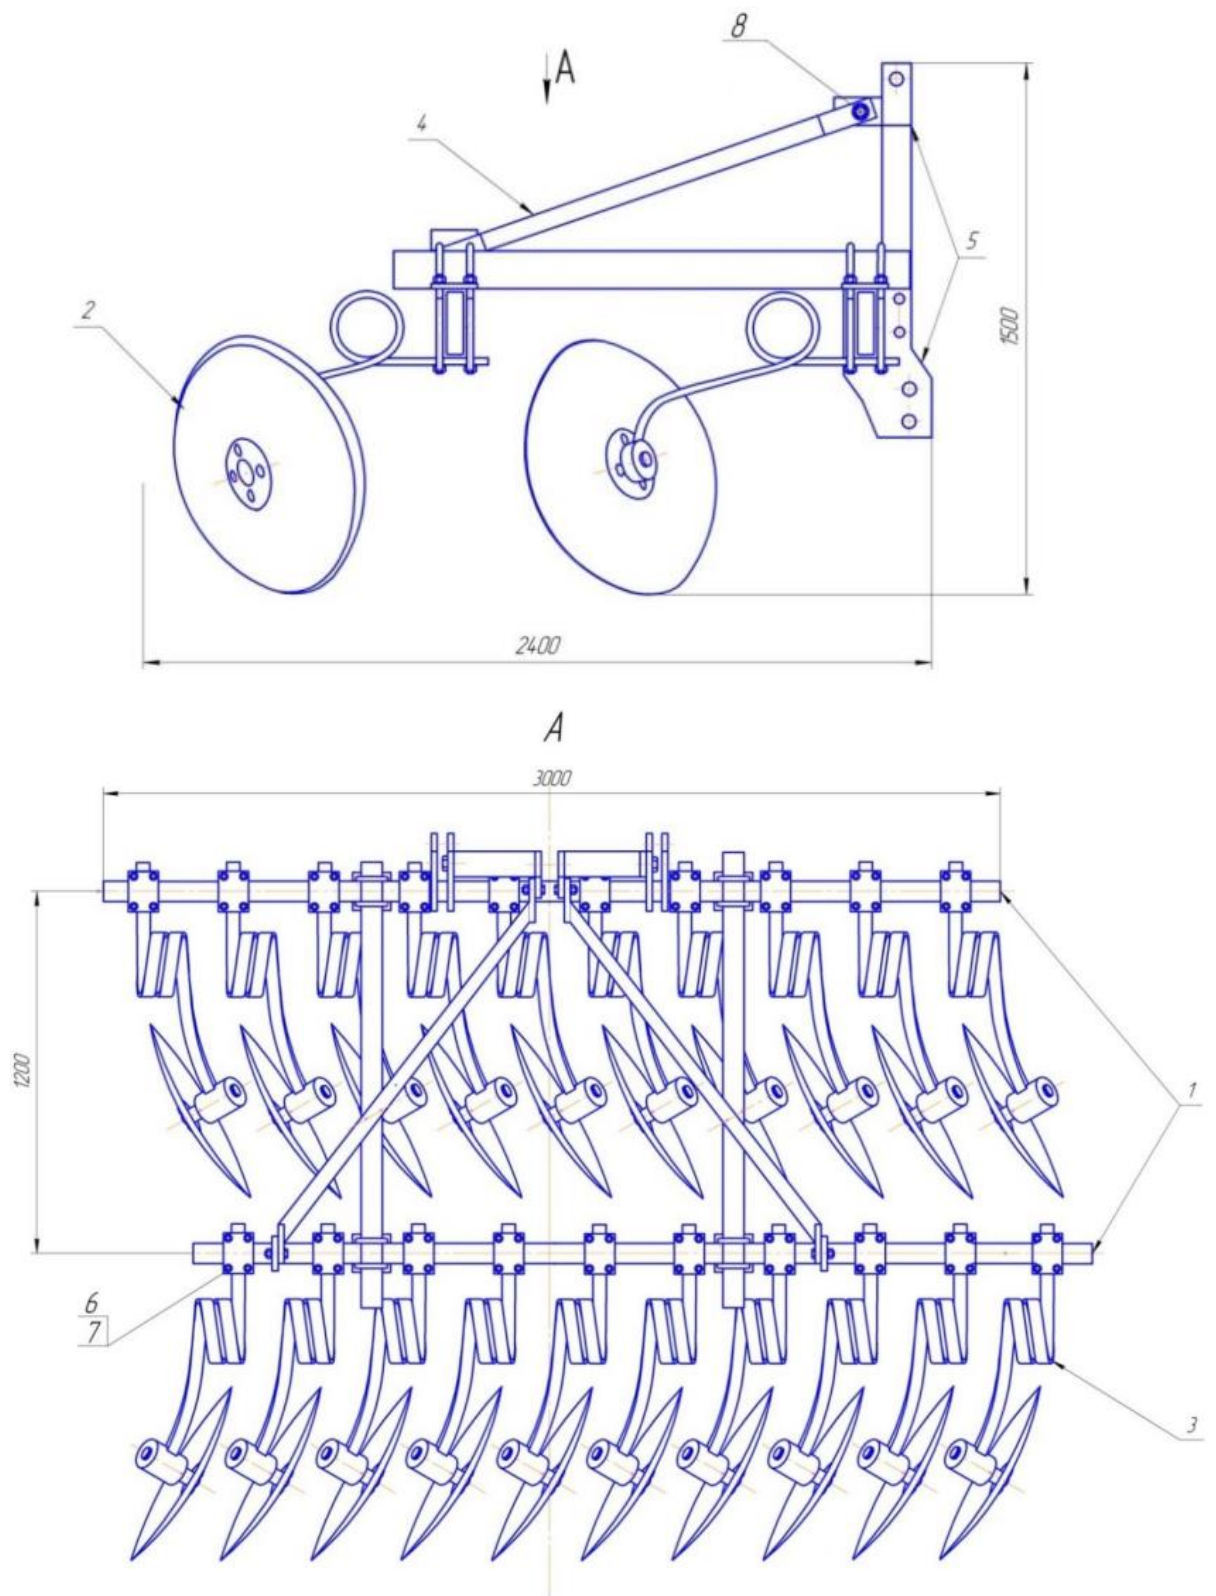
Прецизійний лушительник (загальний вигляд). Склад: 1) рама; 2) робочі диски; 3) запобіжні пружини; 4) тяги; 5, 6) навіски; 7) кріплення; 8) механізм регулювання
